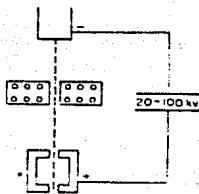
Soldadura por haz de electrones acelerados.
